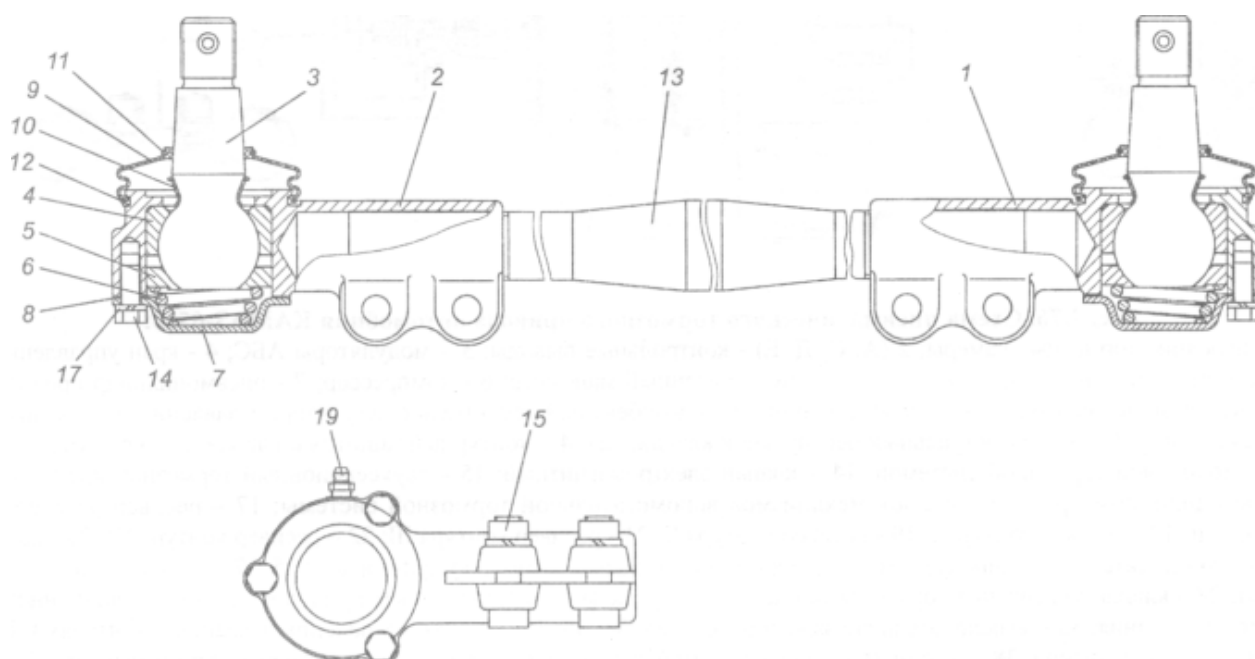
Тяга сошки: 1 - тяга с наконечником и вилкой; 2 - крышка тяги сошки; 3 - палец шаровой; 6 - вкладыш нижний; 7 - пружина; 10 - чехол защитный; 11 - уплотнитель; 12, 13 - кольцо; 14 - шайба; 15 - масленка; 16 - вилка.
